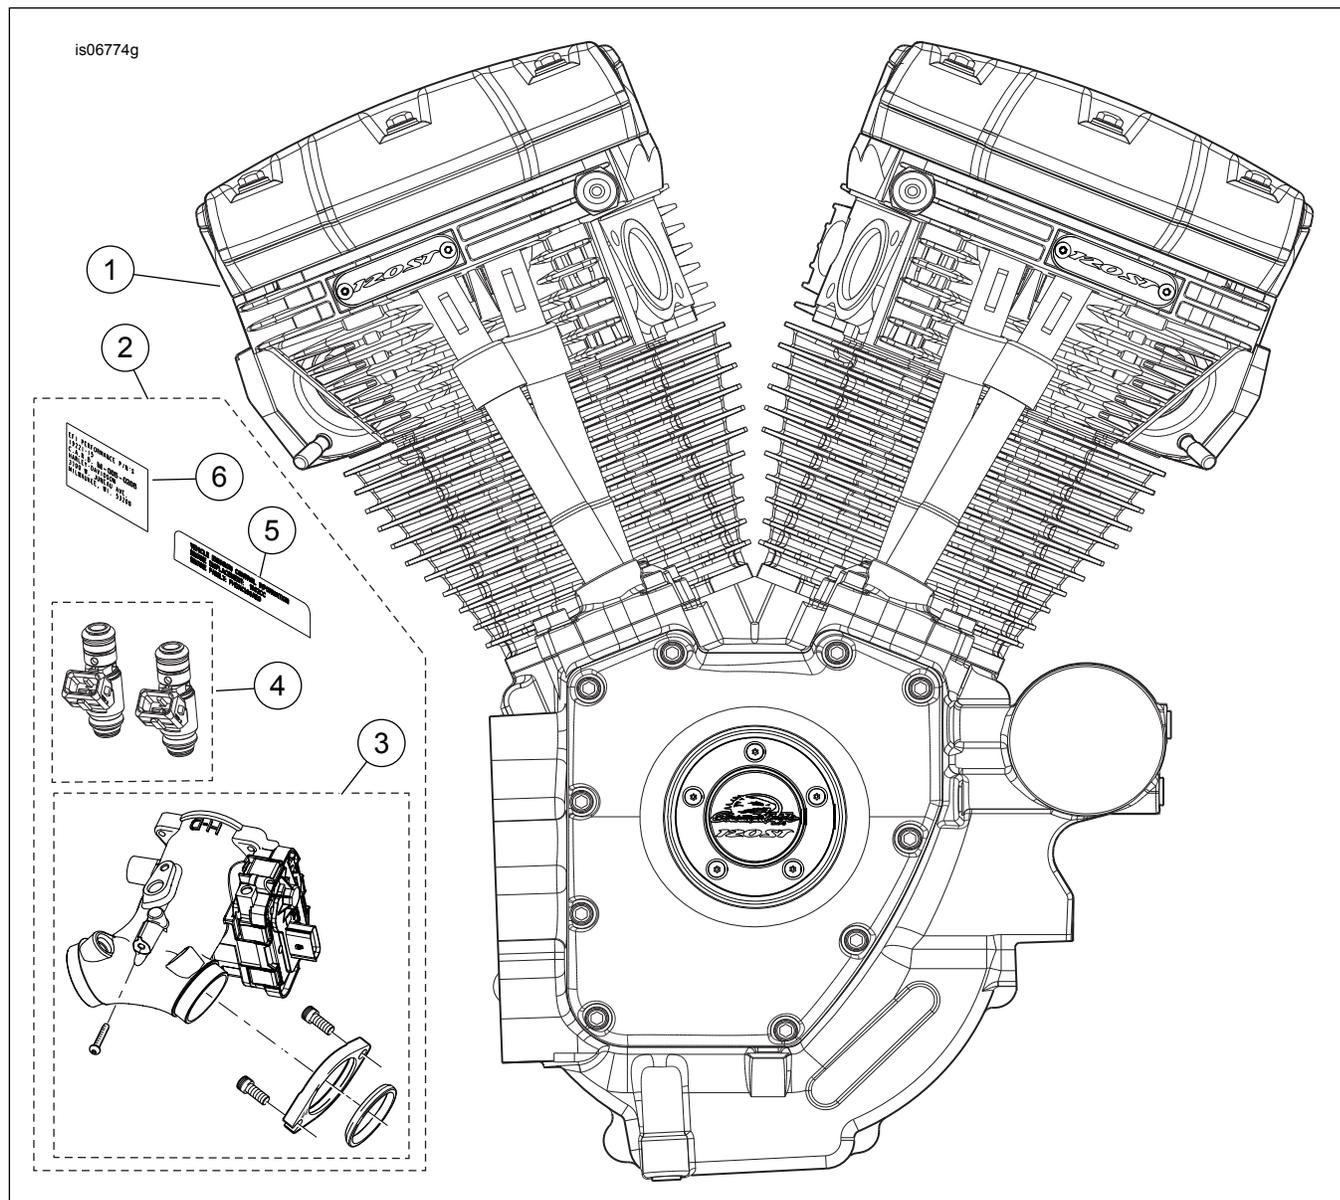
Conjunto motor, Screamin' Eagle 120ST Crate Engine completo
